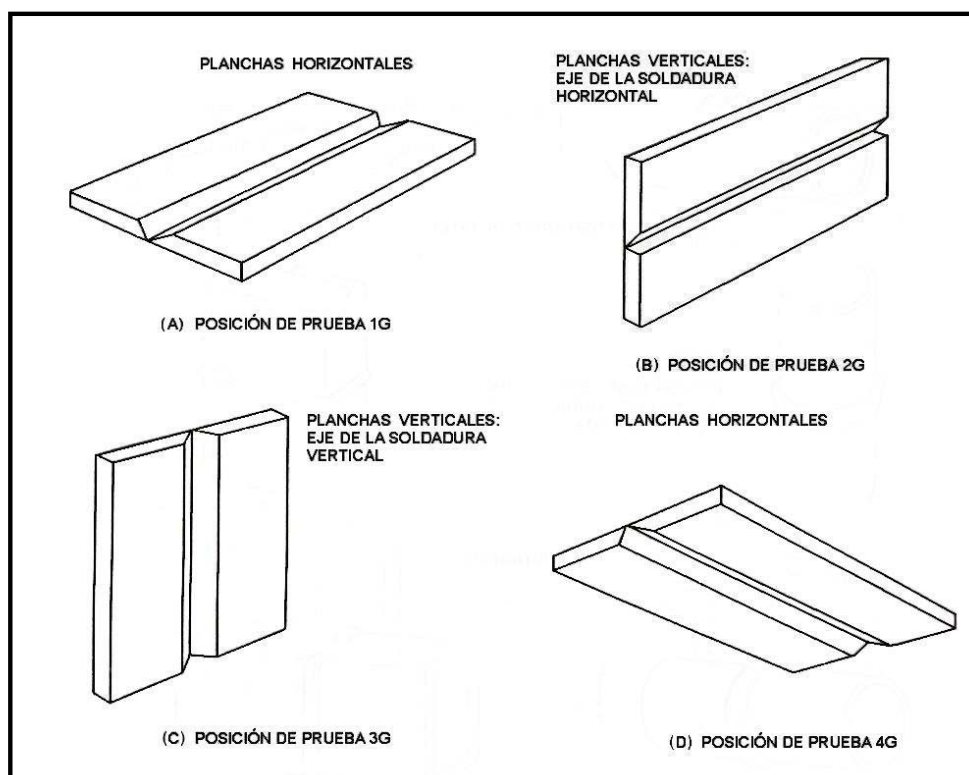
POSICIONES DE SOLDADURA DE RANURA EN PLANCHA PARA CALIFICACIÓN (3)
